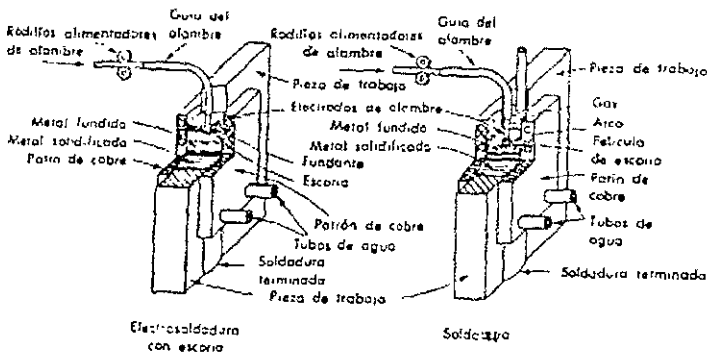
Dos formas de Soldadura Vertical.
